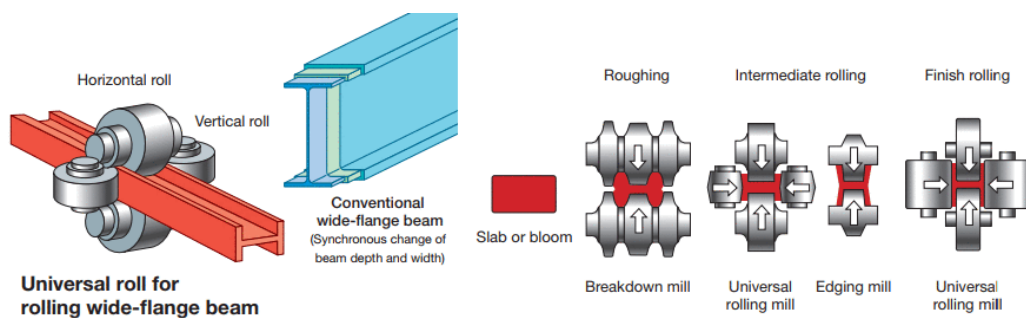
Proceso de laminado en caliente de una viga con sección I
